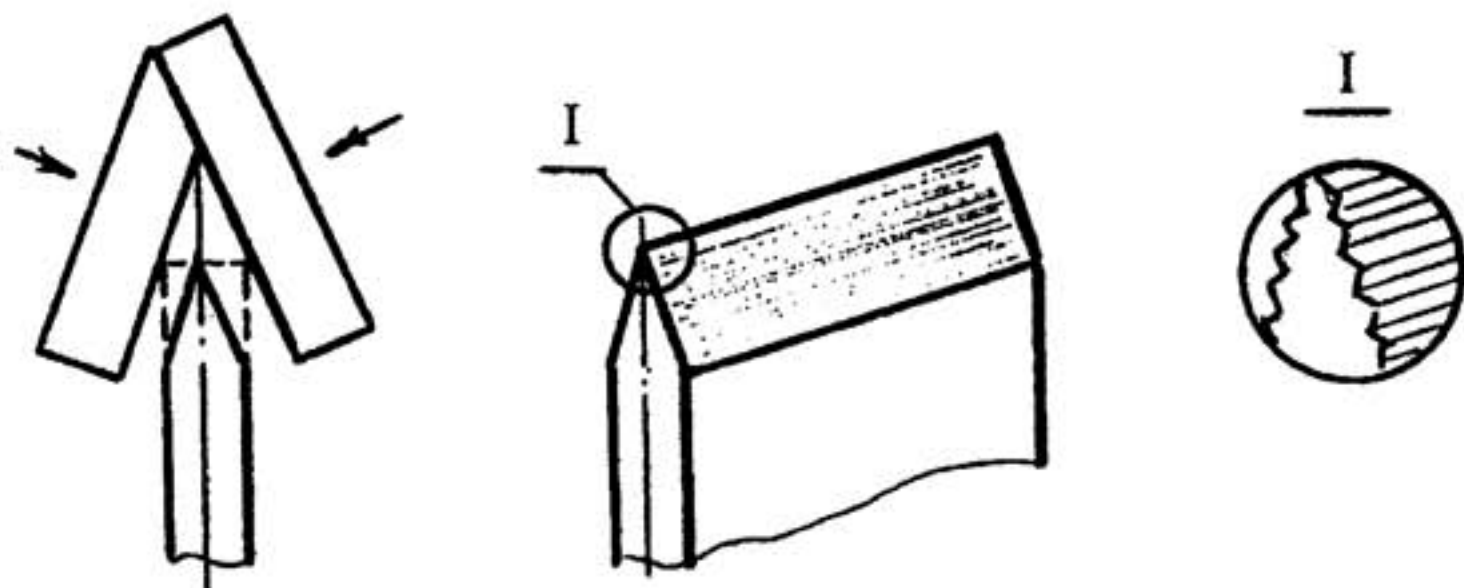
Режущие ножи, изготовленные протяжкой
